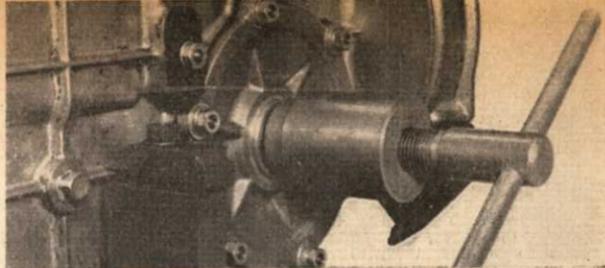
Montage des joints d'étanchéité avec l'outil 1.050
